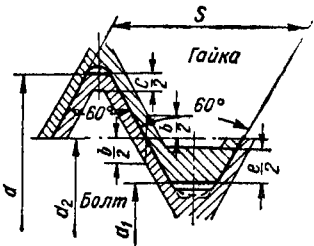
Схема расположения полей допусков метрической резьбы.
